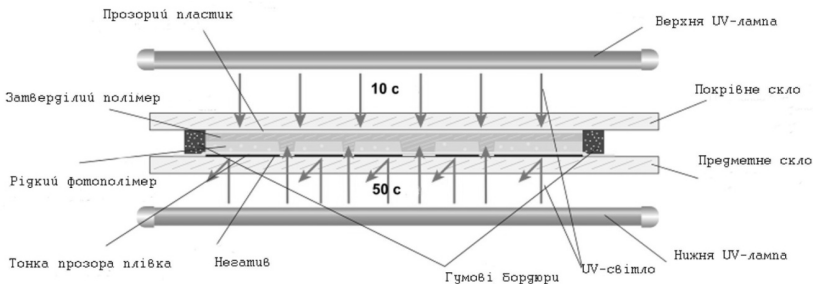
Схема виготовлення кліше печатки з використанням рідкого фотополімерного матеріалу
